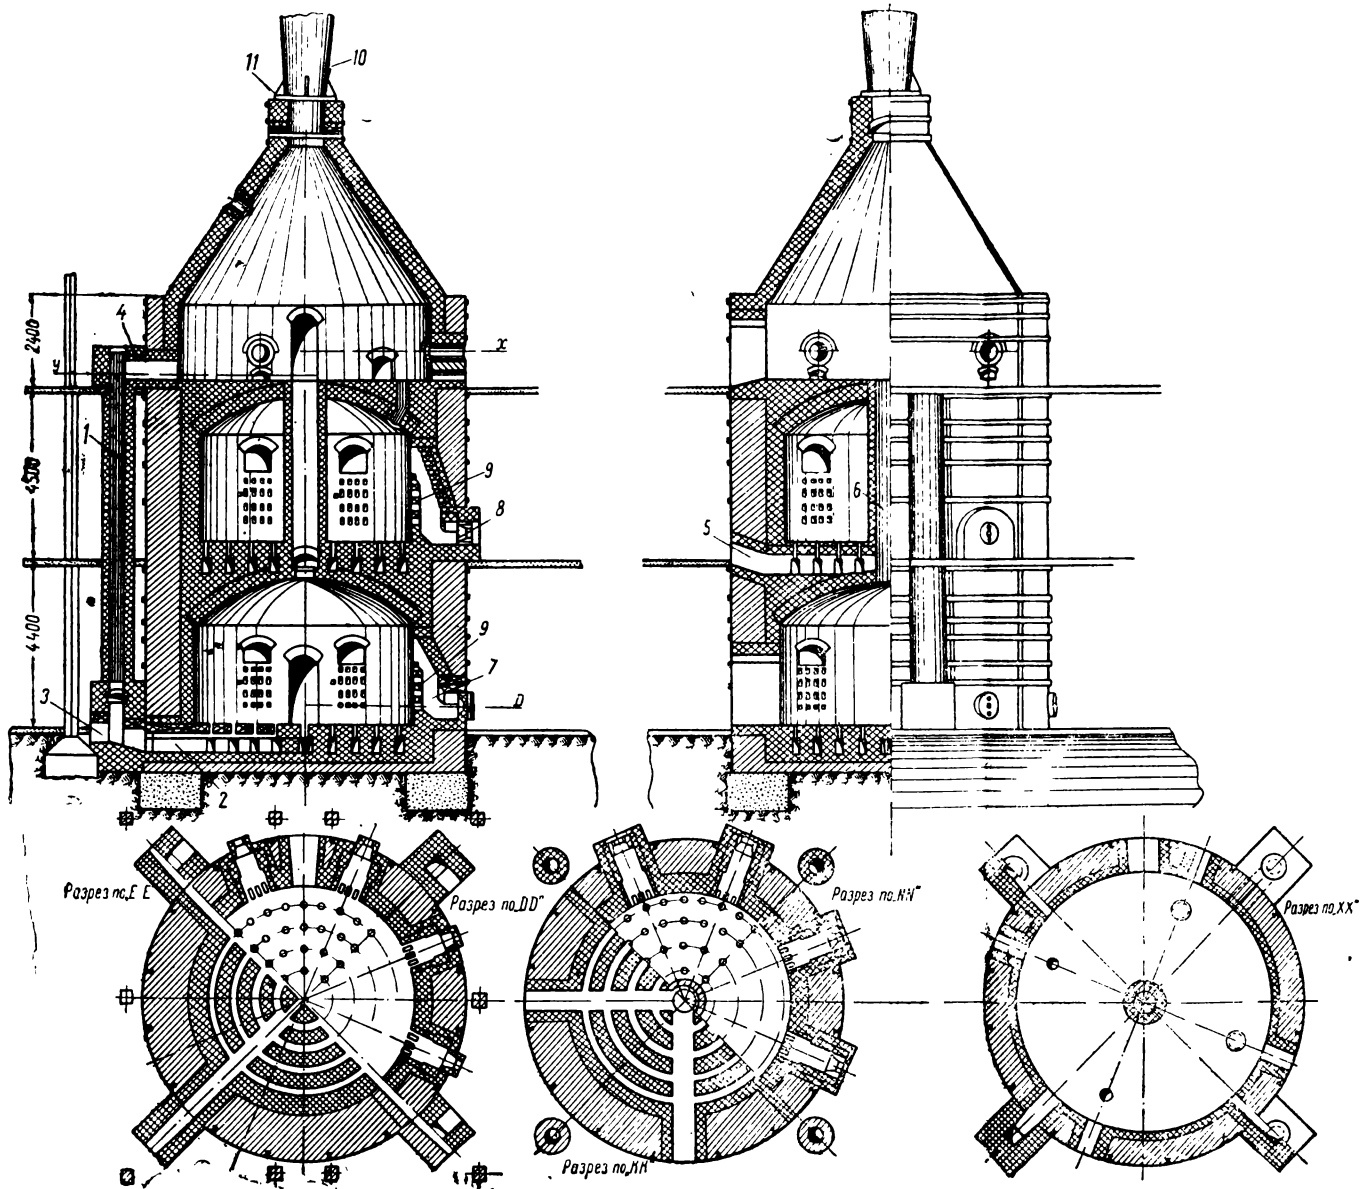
Двухэтажный горн для обжига изоляторов с мазутными топками и выносными вертикальными каналами.
